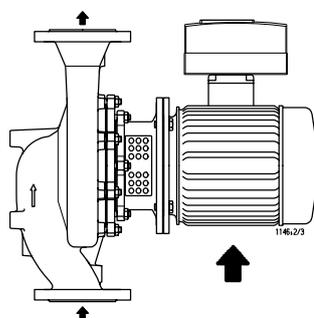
Montagem na horizontal do grupo electrobomba com PumpDrive, sentido do fluxo de baixo para cima
